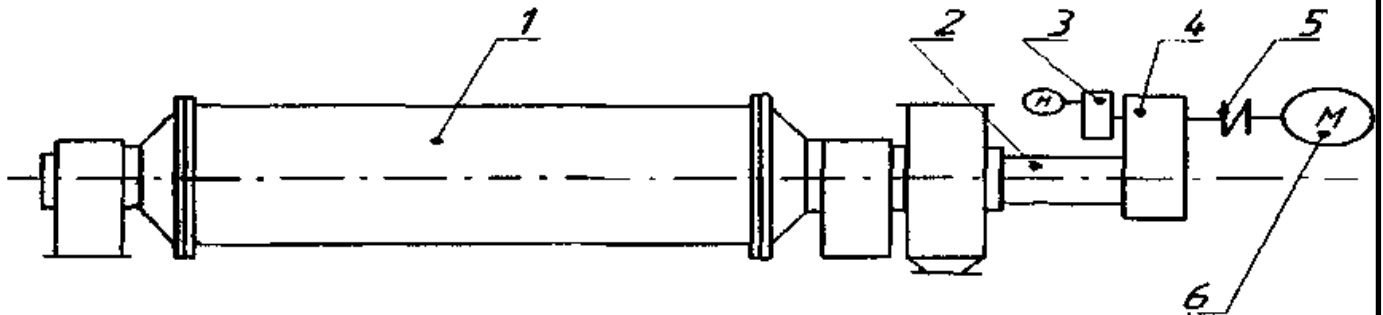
Кінематична схема привода 1 - трубний млин; 2 - вал приводний; 3 - привод допоміжний; 4 - редуктор; 5 - муфта; 6 – електродвигун
